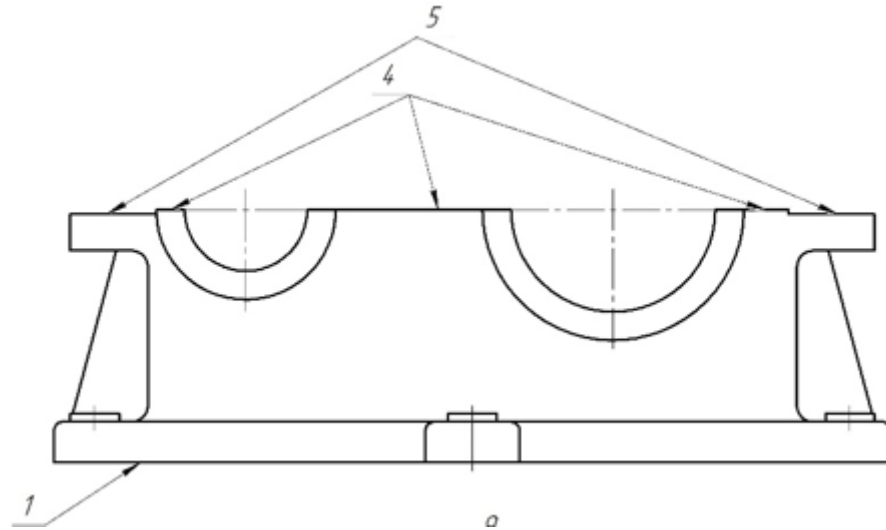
Нумерація оброблюваних поверхонь деталі «Корпус редуктора»
